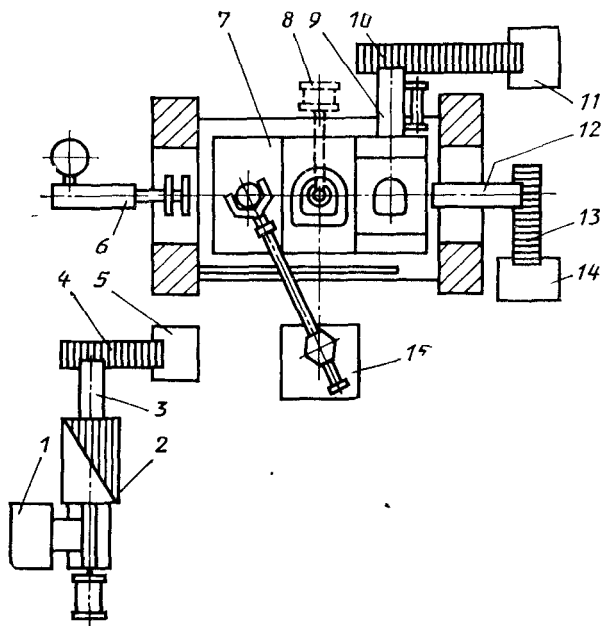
Компоновка РТК на базе КГШП с фронтальным расположением манипулятора ПР
